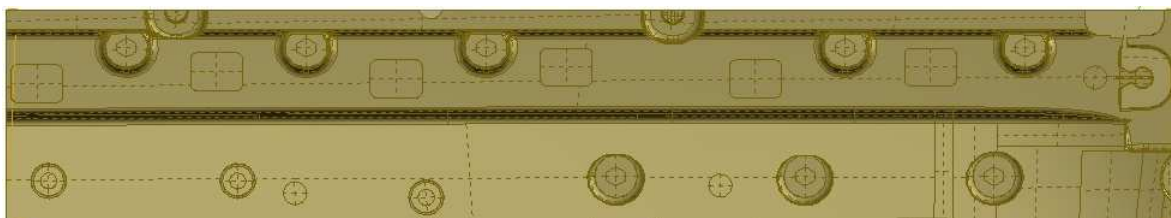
Upnutí testovací desky na stole portálové frézky [5]
